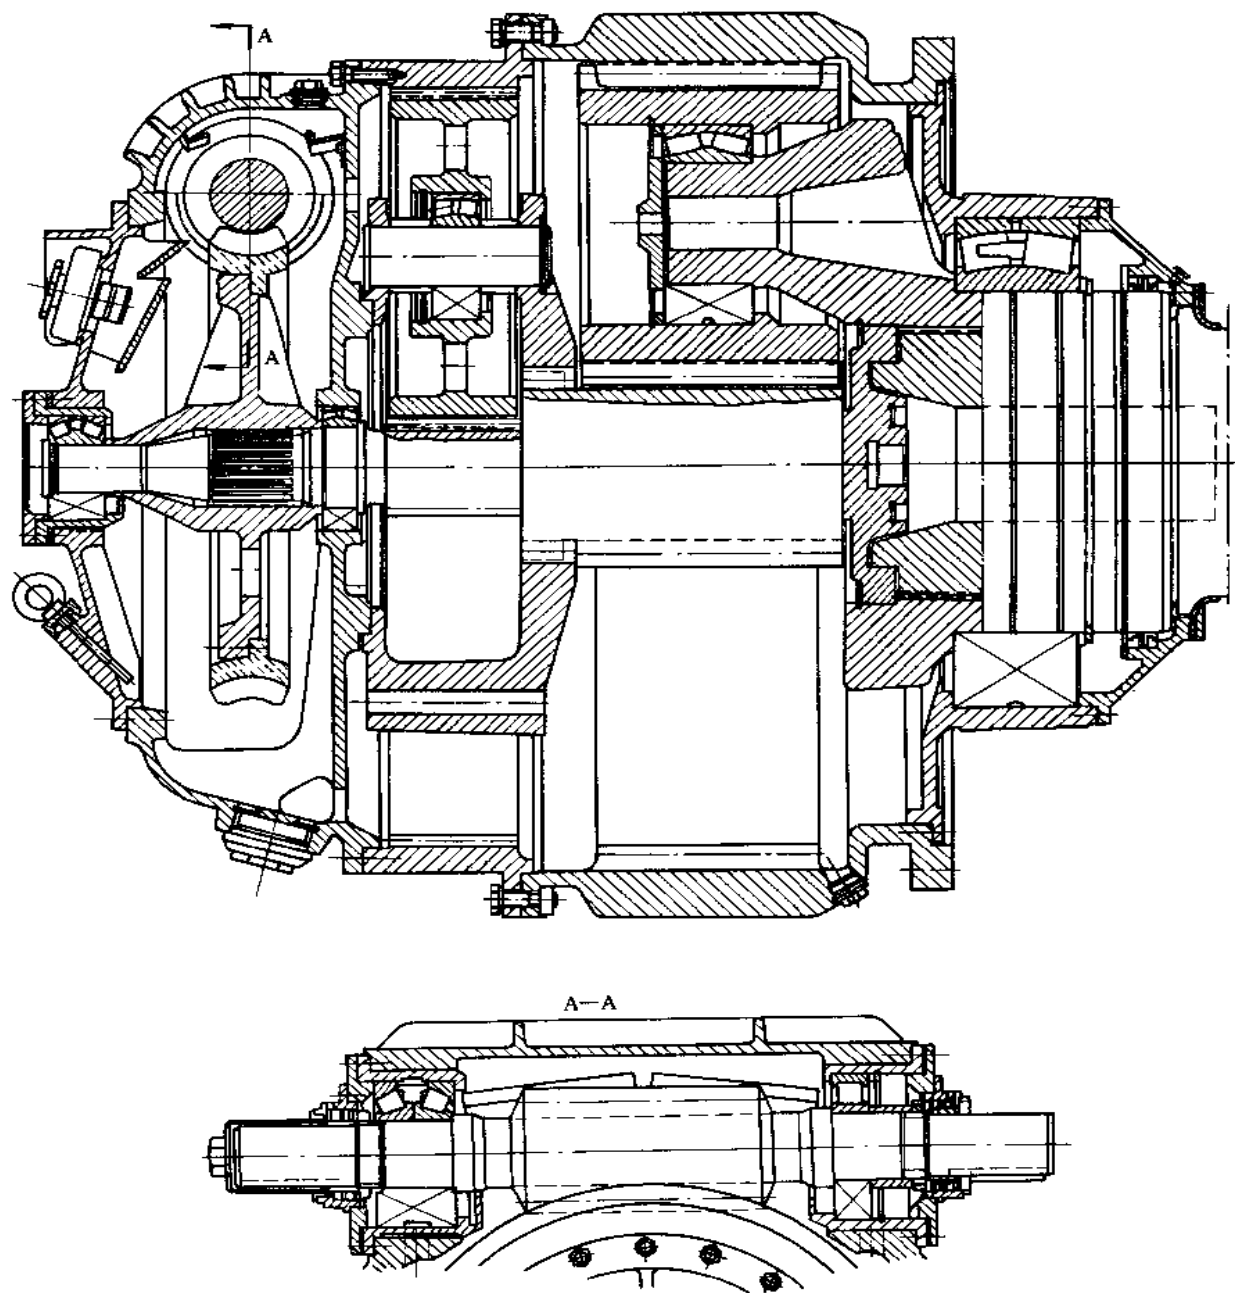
用于斗轮挖掘机履带传动的蜗轮-行星齿轮轴支承
